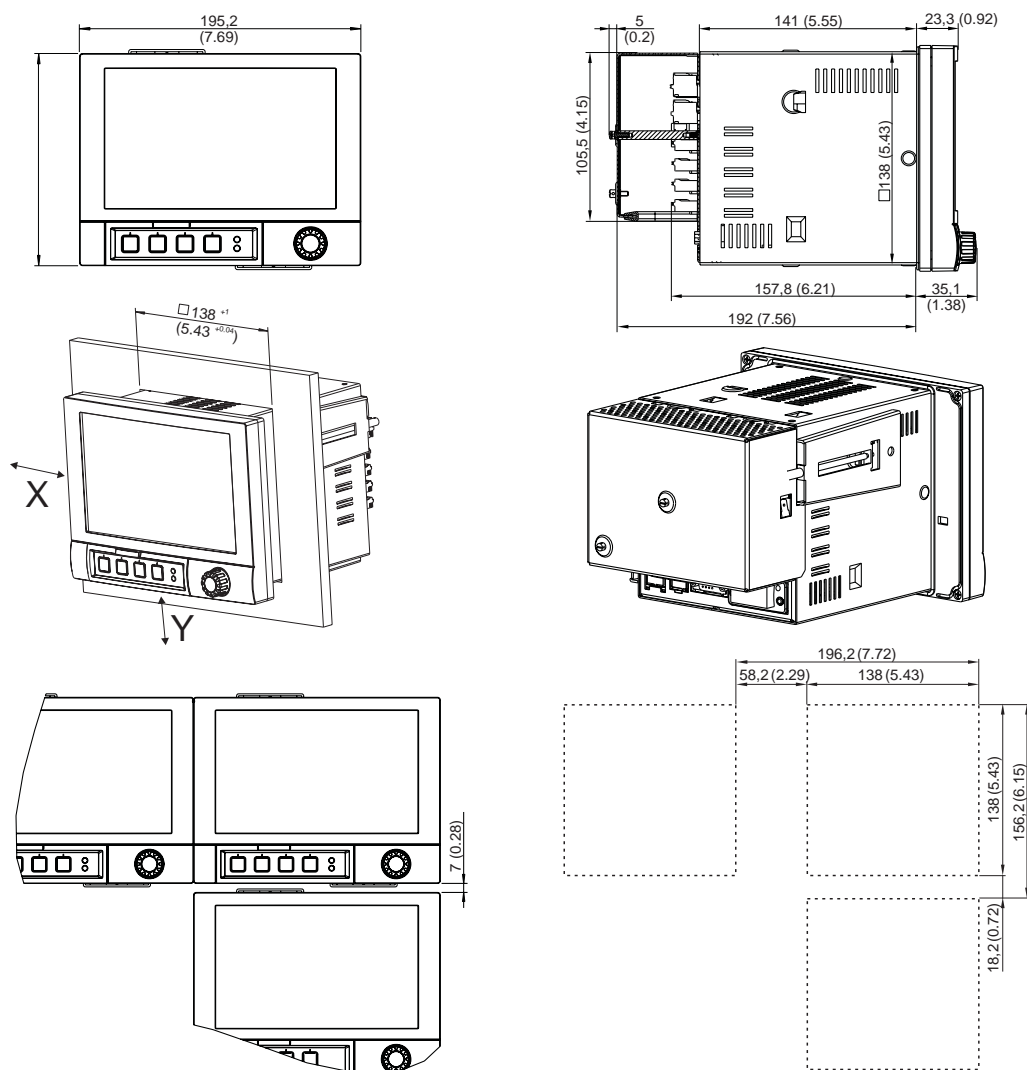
Montaje en armario y dimensiones para la instalación. Todas las dimensiones se especifican en mm (o pulgadas)
